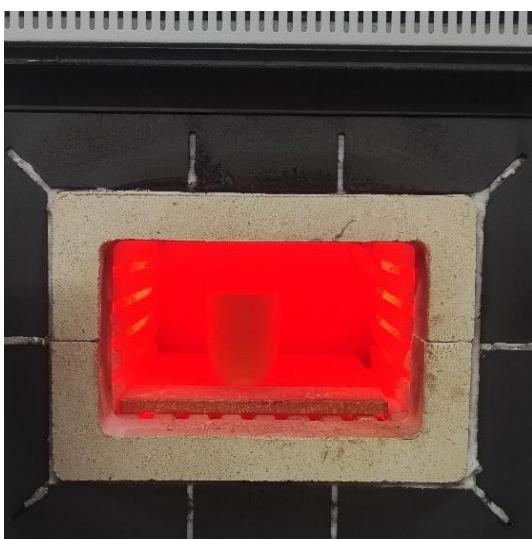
Плавка и внешний вид слитков сплавов легких и рассеянных металлов
